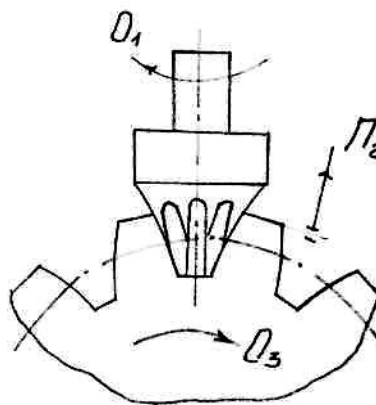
Схема обробки пальчиковою фрезою.
